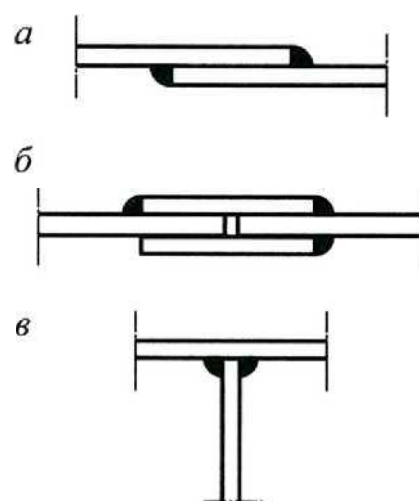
Сварные соединения: а — внахлестку; б — с накладками; в — в тавр
